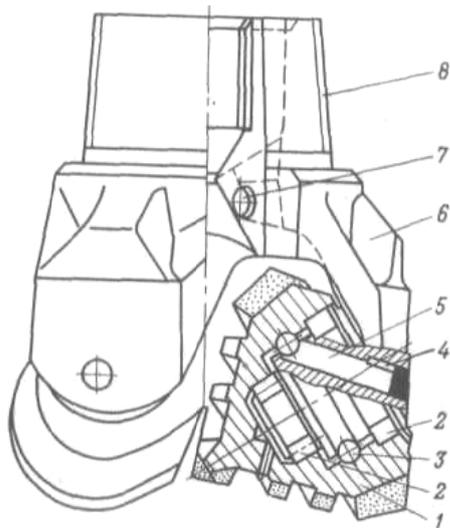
Схема конструкции трехшарошечного секционного долота с фрезерованными зубьями, наплавленными твердым сплавом: 1 – шарошка; 2 – ролики; 3 – шарик; 4, 7 – штифты; 5 – палец; 6 – лапа; 8 – базовая присоединительная резьба, расположенная на ниппельной части долота
